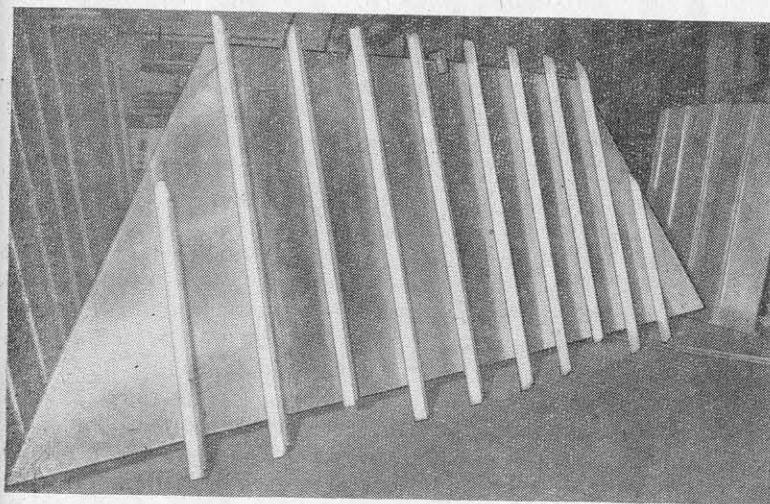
Переборка, сваренная контактной сваркой.
